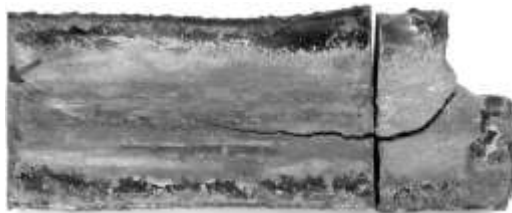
Fratura em estrutura soldada revestida com zinco [5].
